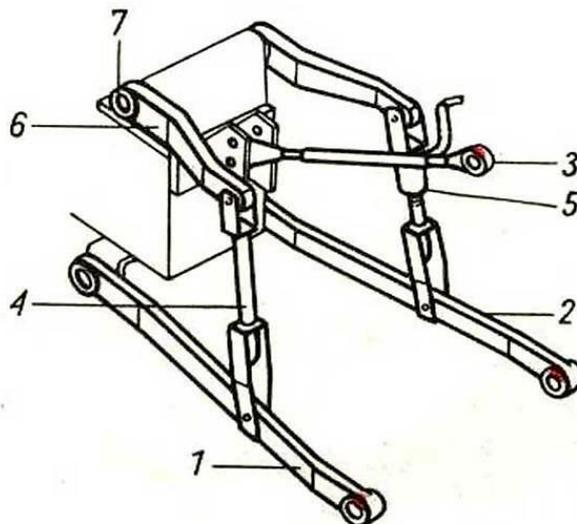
Attelage trois-points du tracteur : 1, 2 – barres inférieures, 3 – point d'attelage supérieur, 4 – chandelle gauche, 5 – chandelle droite réglable, 6 – bras de relevage, 7 – arbre de relevage
